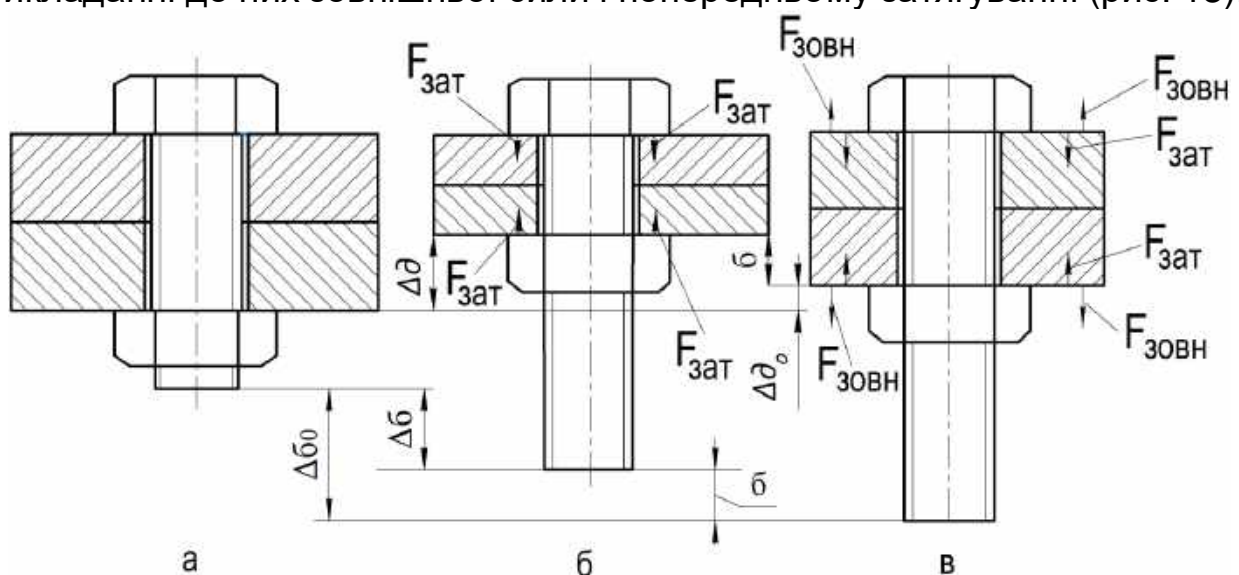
Різні стани болта і деталей, що з'єднуються:
